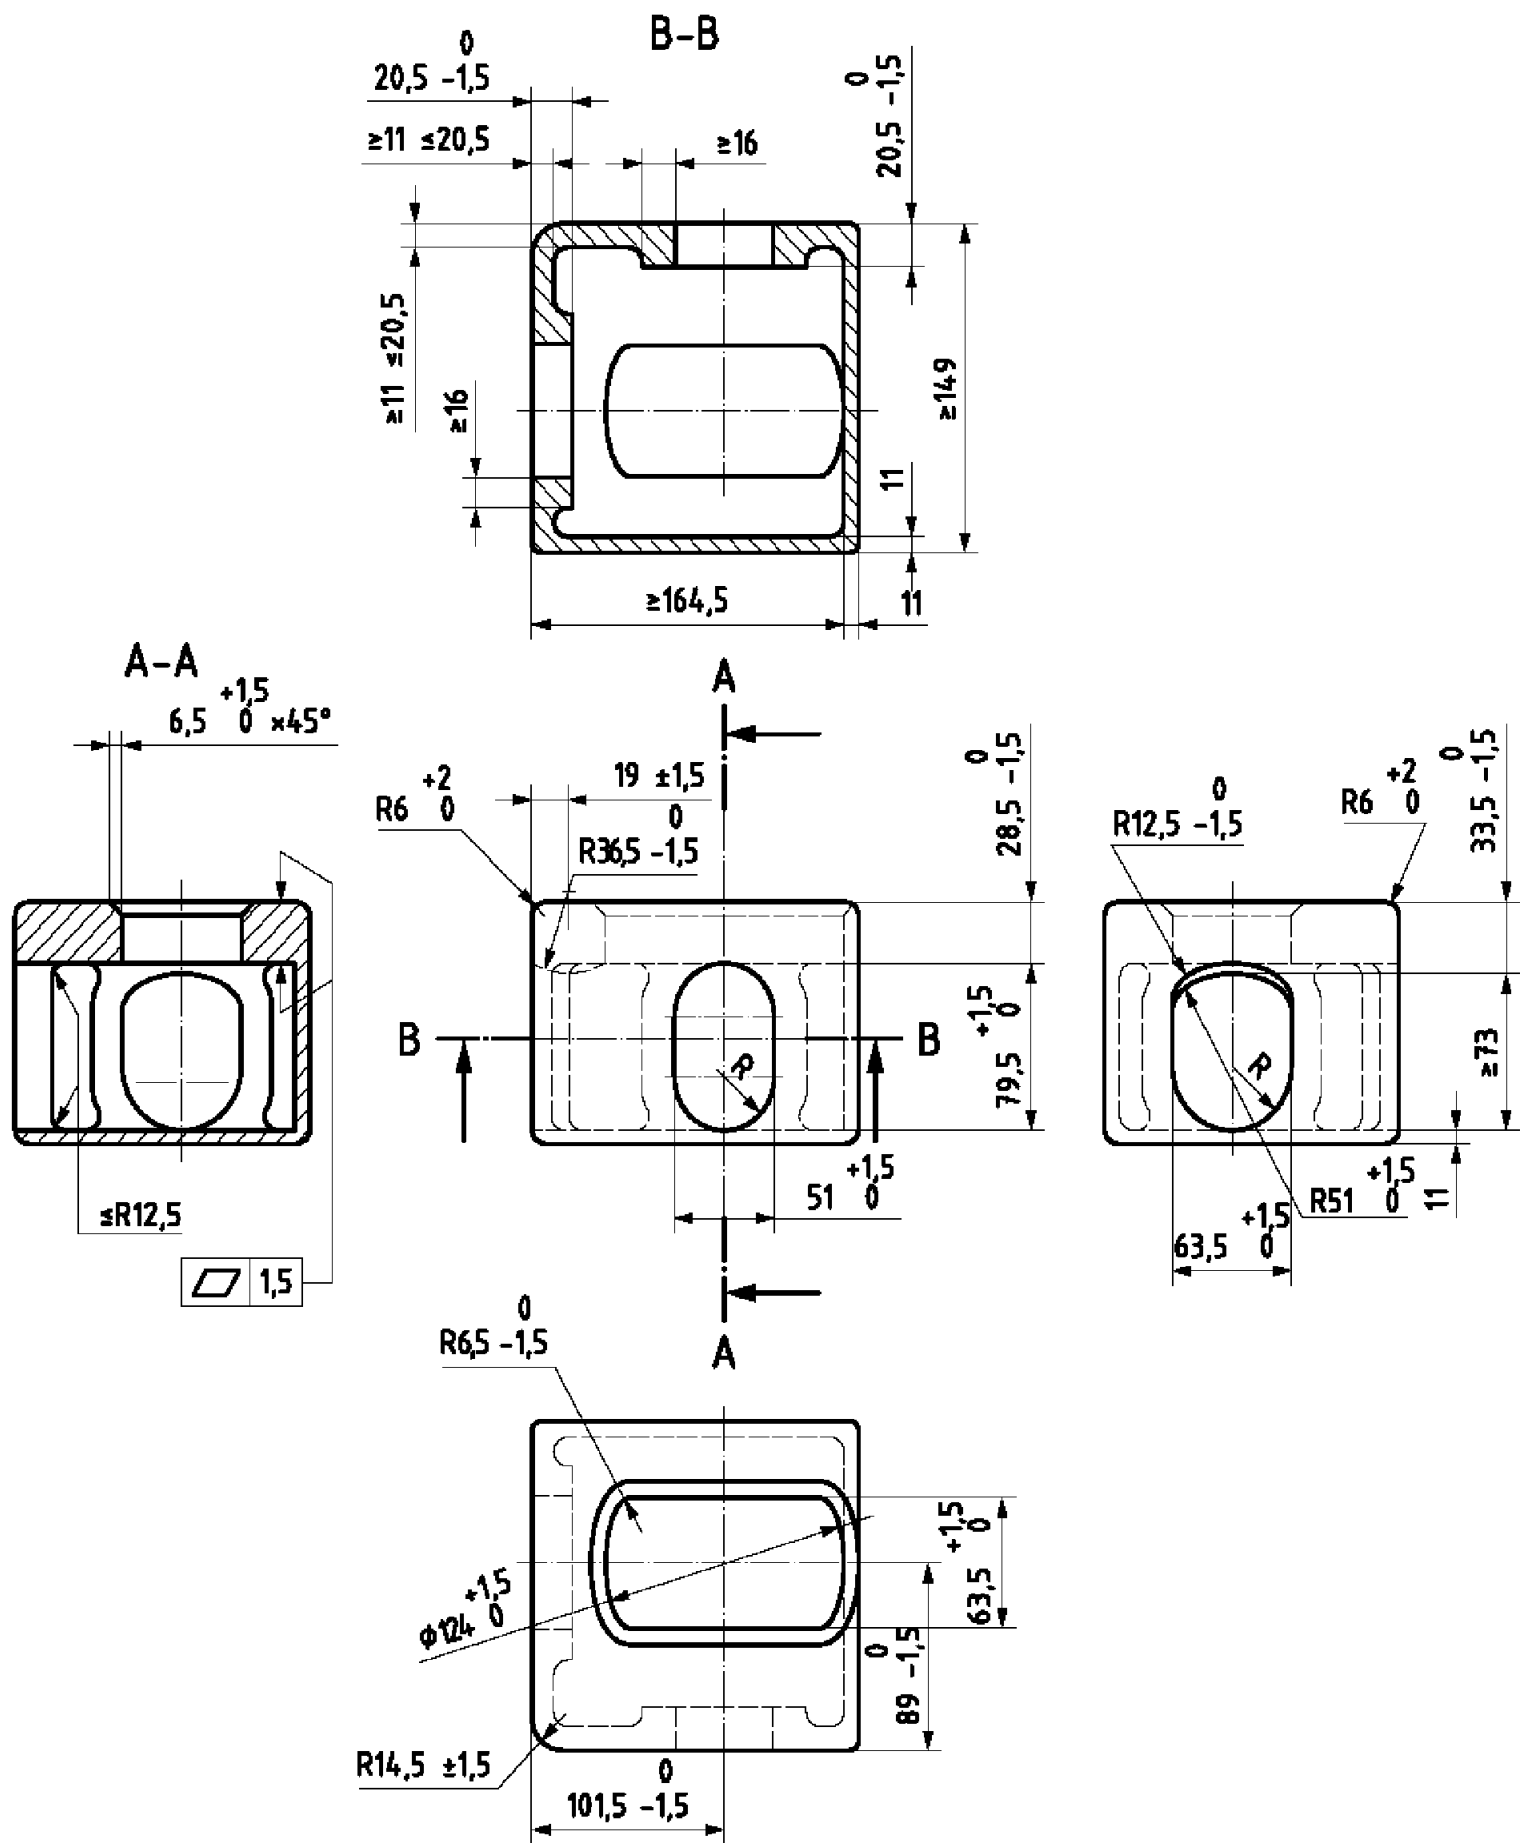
Верхний угловой фитинг, мм:
